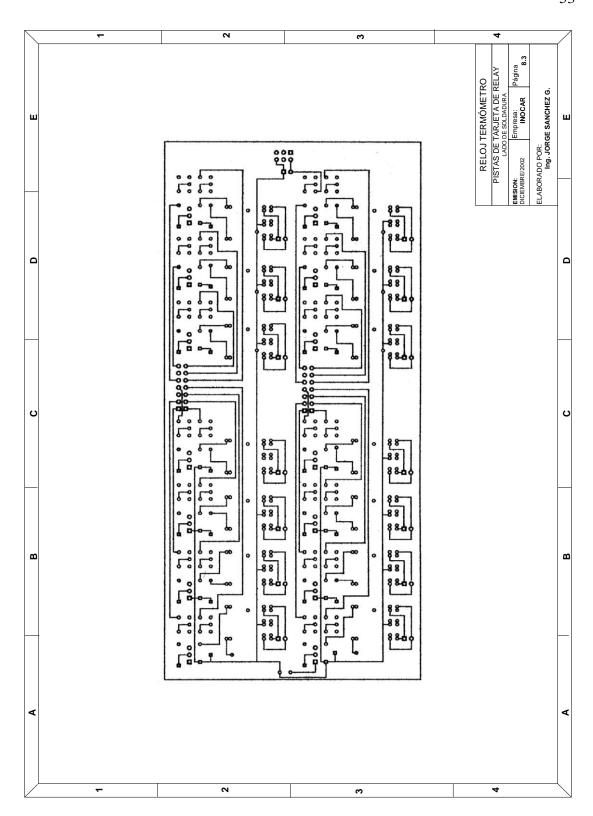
Tarjeta de relay (Pistas lado de soldadura)
